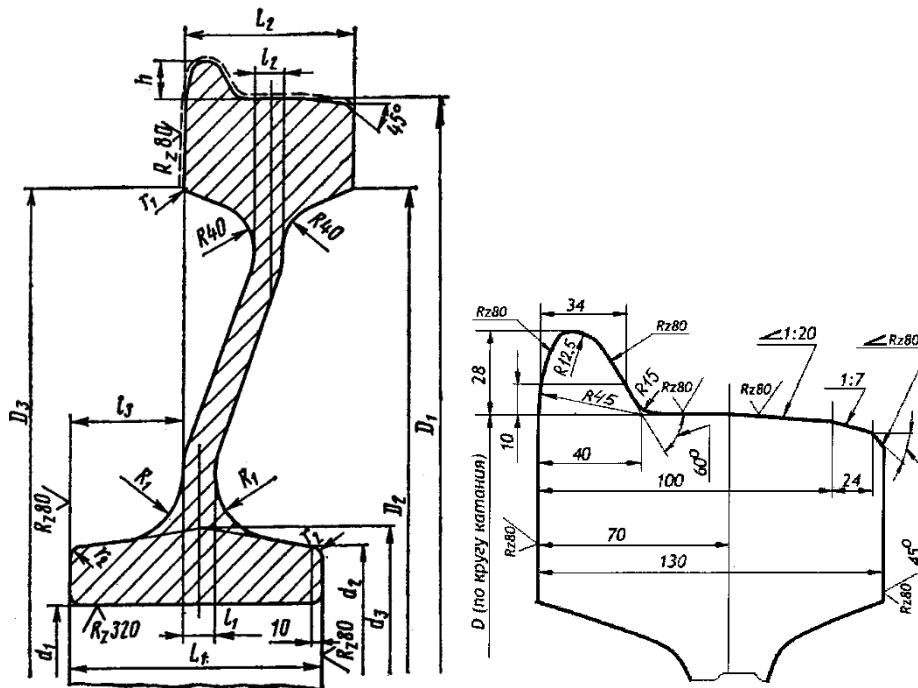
Цельнокатаное колесо и профиль поверхности катания колеса для вагонов со скоростями до 160 км/час
